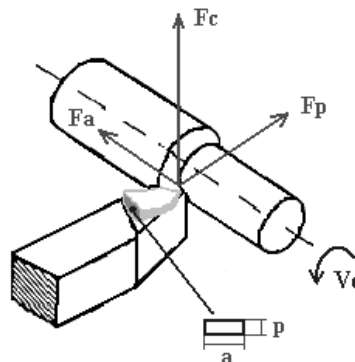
Fuerzas que ejerce la herramienta sobre la pieza.
